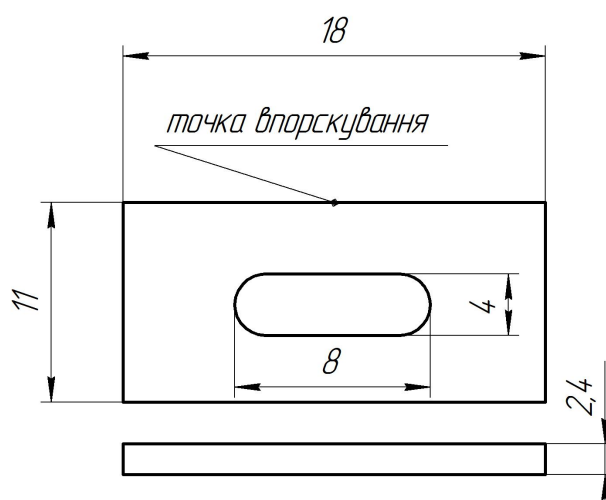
Ескіз деталі та розташування точки впорскування
